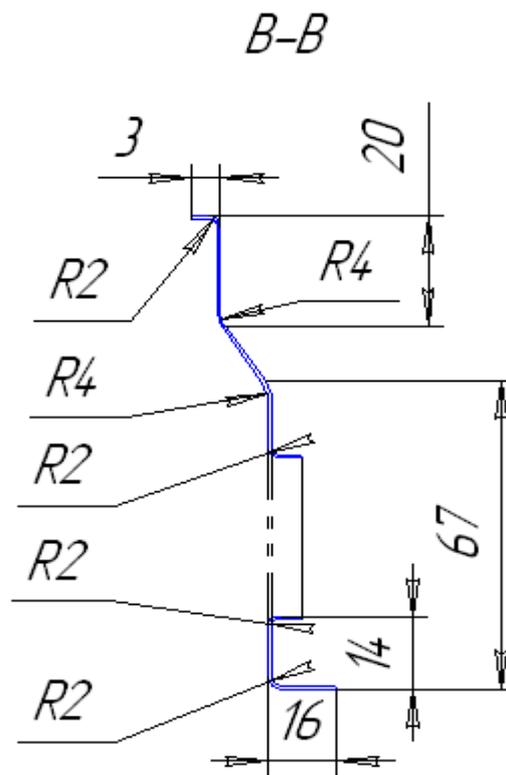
(в, г) - Определение размеров заготовки в поперечном направлении
